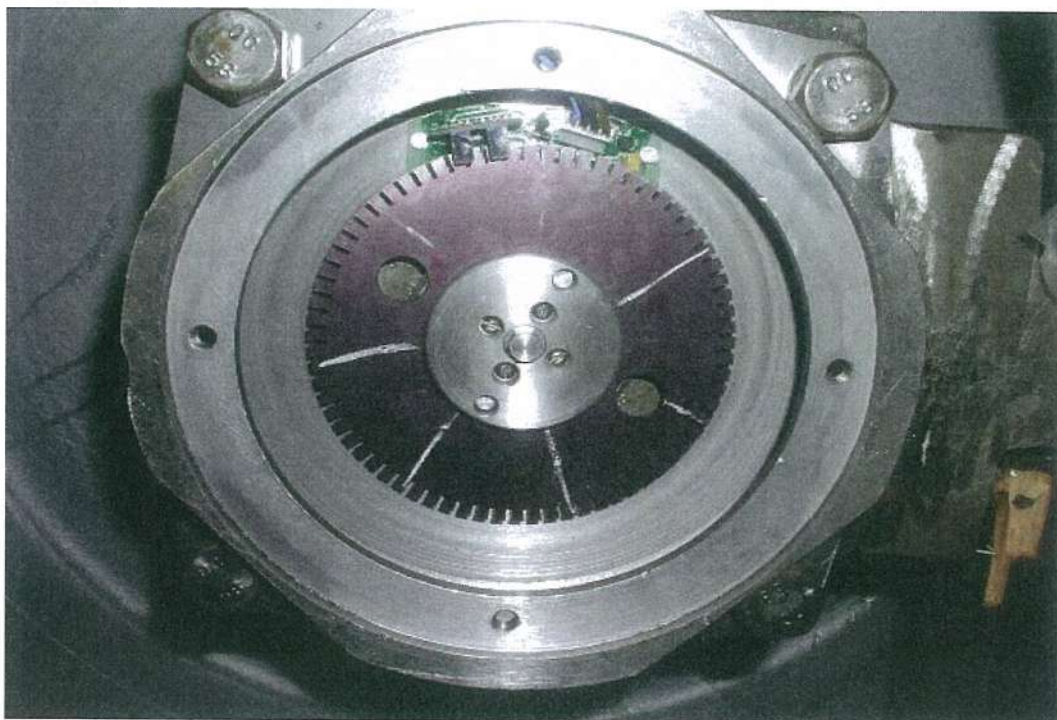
Зчитувальний пристрій датчика обертів колеса
